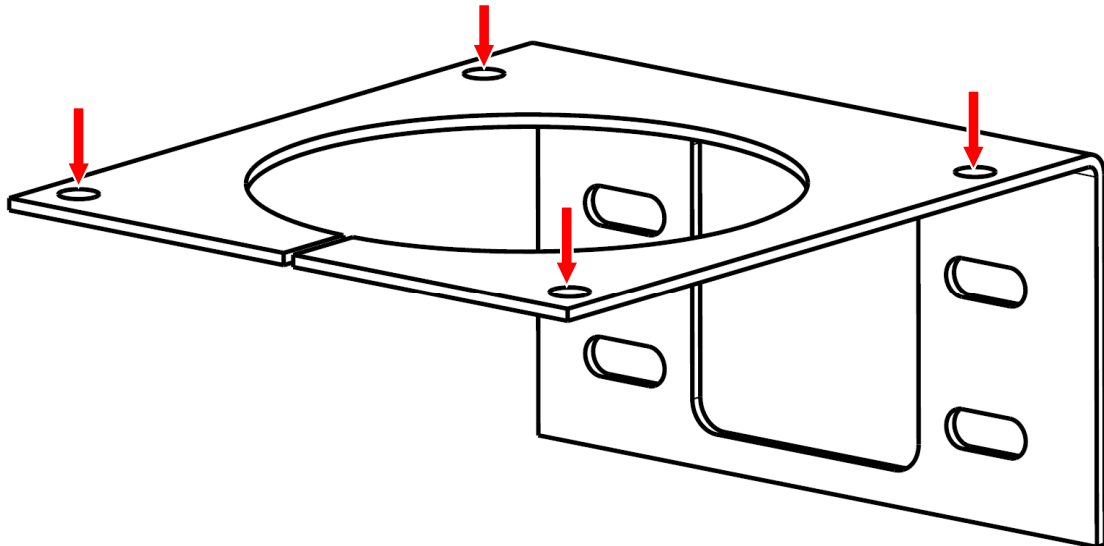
Wandlermontageblech mit Befestigungspunkten (L-Profilteil PLB029-377330)
